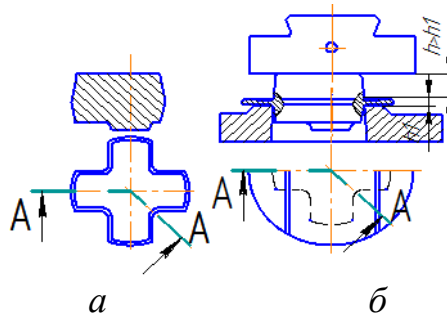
Покованка повідні хрестоподібної форми (а); конструкція робочих частин штампа за раціоналізаторською пропозицією з циліндричним пуансоном спрощеної форми (б)
